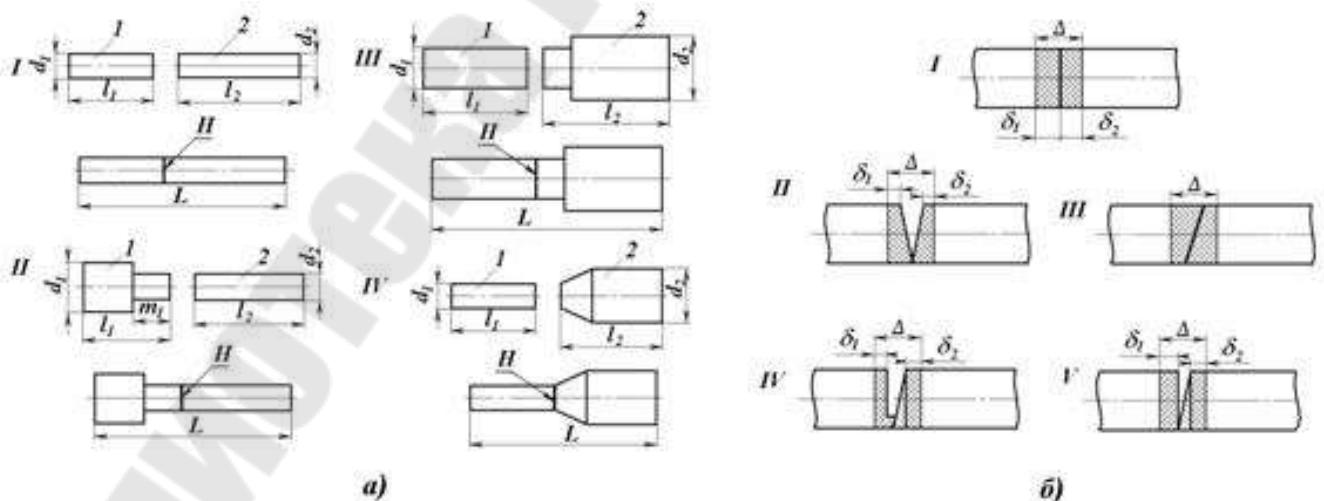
Эскизы заготовок для сварки концевого инструмента (а) и влияние перекоса торца, а также взаимной их ориентации на величину припуска  $\Delta$  ( $\delta_1$  и  $\delta_2$  припуски на сварку рабочей и хвостовой части инструмента) при сварке (б)
